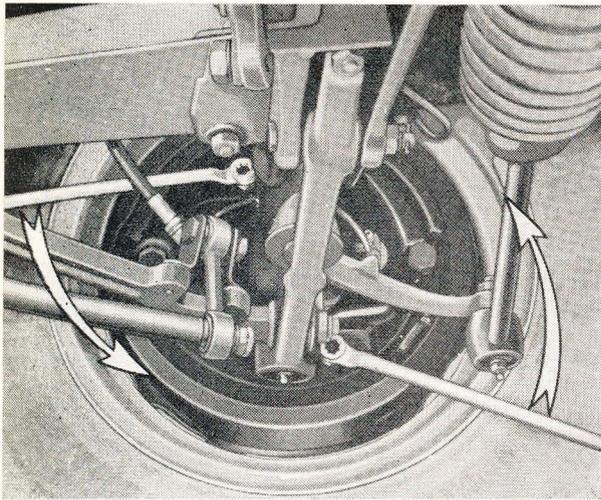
Réglage des freins AV thermostables. Sens de rotation des carrés d'excentriques.
